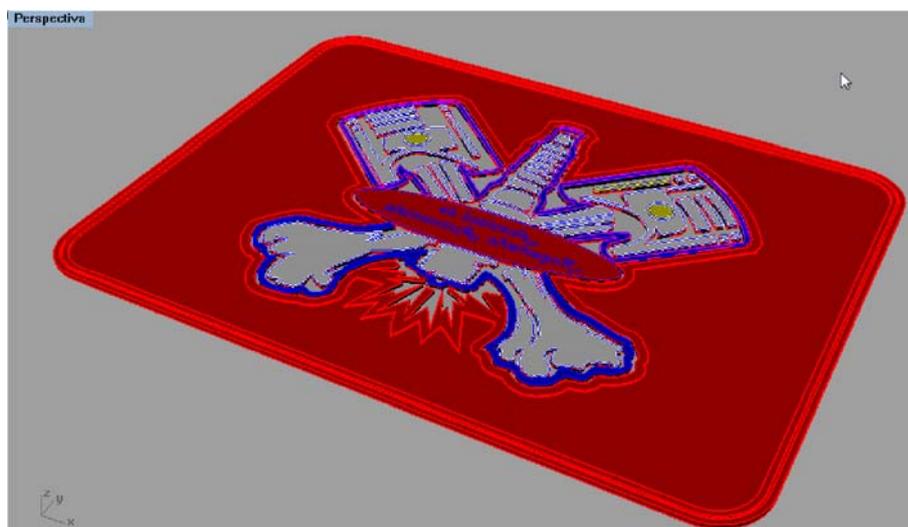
Construcción de la matriz – construcción de las ranuras
